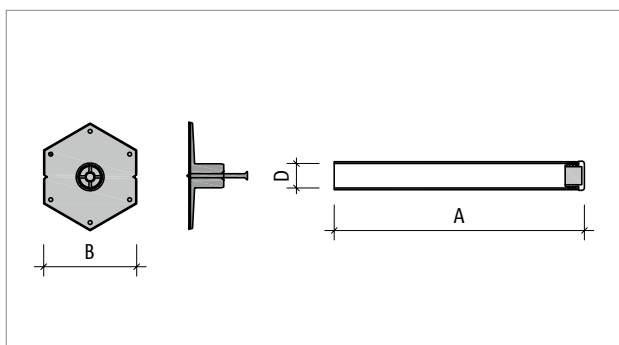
Schöck Stacon® typ LD Part A4, LD Part Zn: Rozměry trnu
